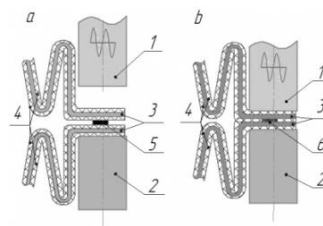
Схема соединения концевых секций фильтровального элемента: а — до УЗ сварки, б — после УЗ сварки; 1 — излучатель, 2 — ложемент, 3 — фильтровальная бумага, 4 — опорные стальные сетки, 5 — вставка из ПВХ, 6 — гибридное соединение (сварной шов)
